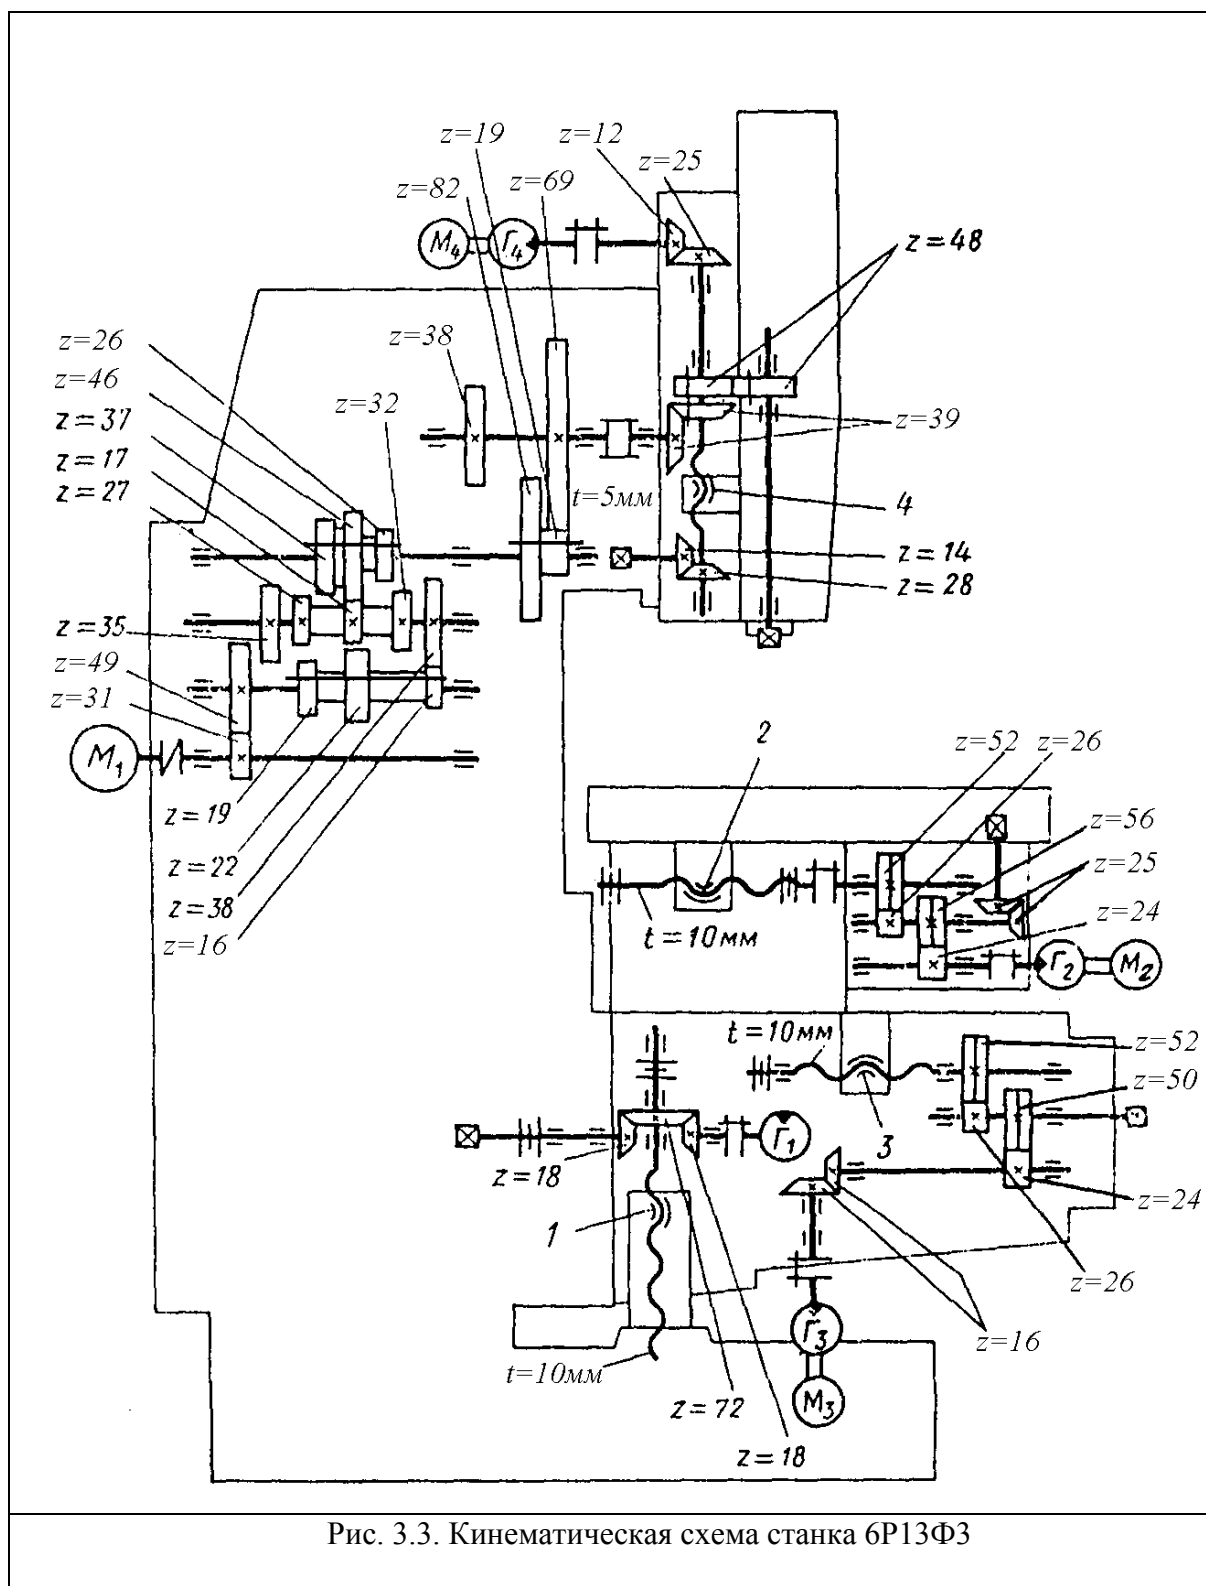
Кинематическая схема станка 6P13Ф3
